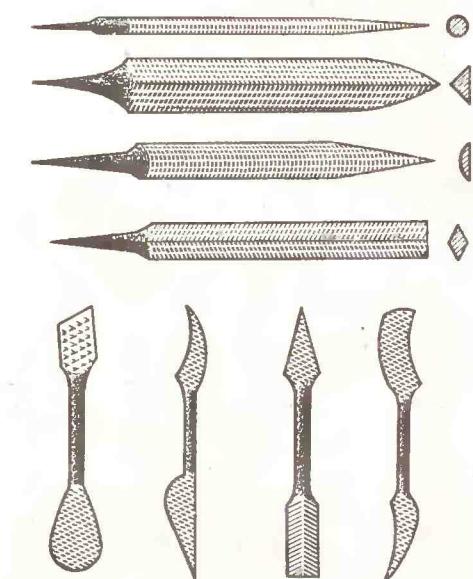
Рашили для зачистки плоскорельефной и рельефной резьбы
